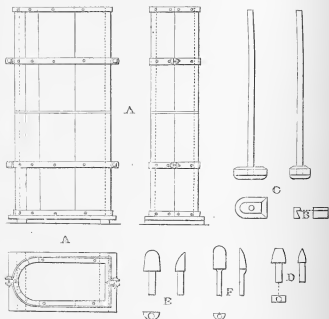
Moule extérieur et outils pour la fabrication des moules silésiens.
